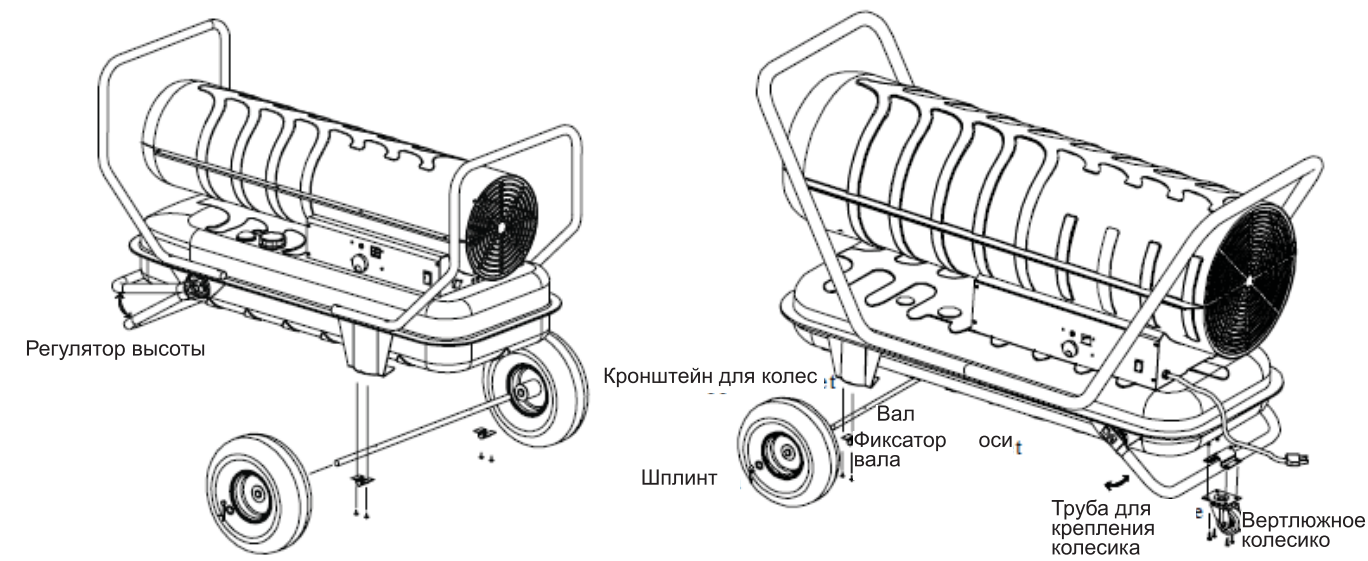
Сборка нагревателей моделей TK-50000, TK-70000, TK-100000
